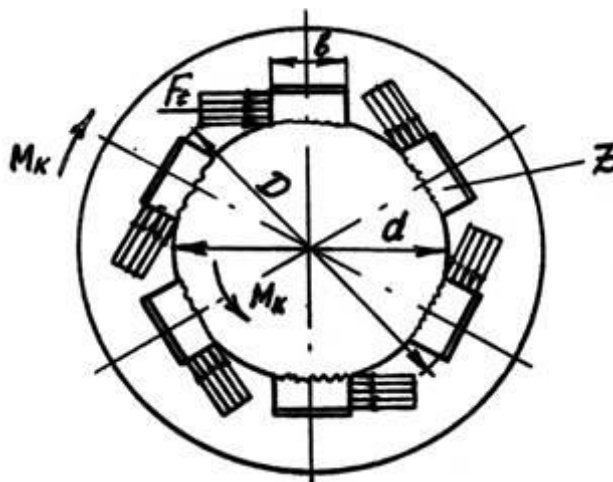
Розрахункова схема шліцьового з'єднання
